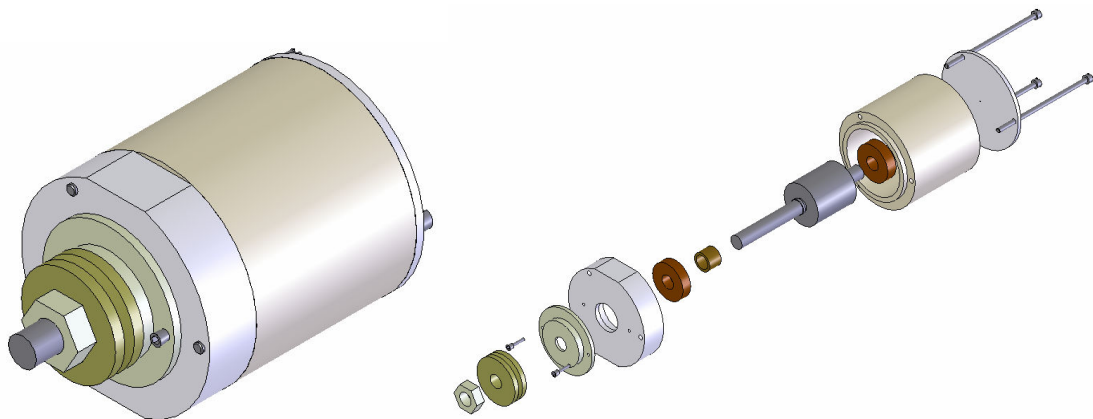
Vue d'ensemble de l'alternateur en position assemblée et vue éclatée de ce même produit.
